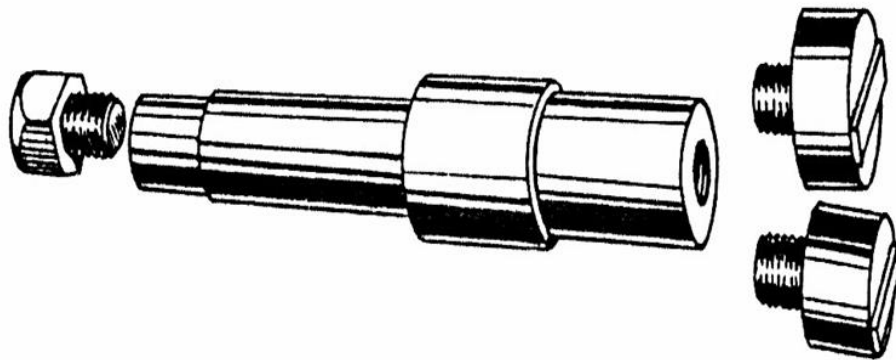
Оправка для ремонту поворотного кулака
